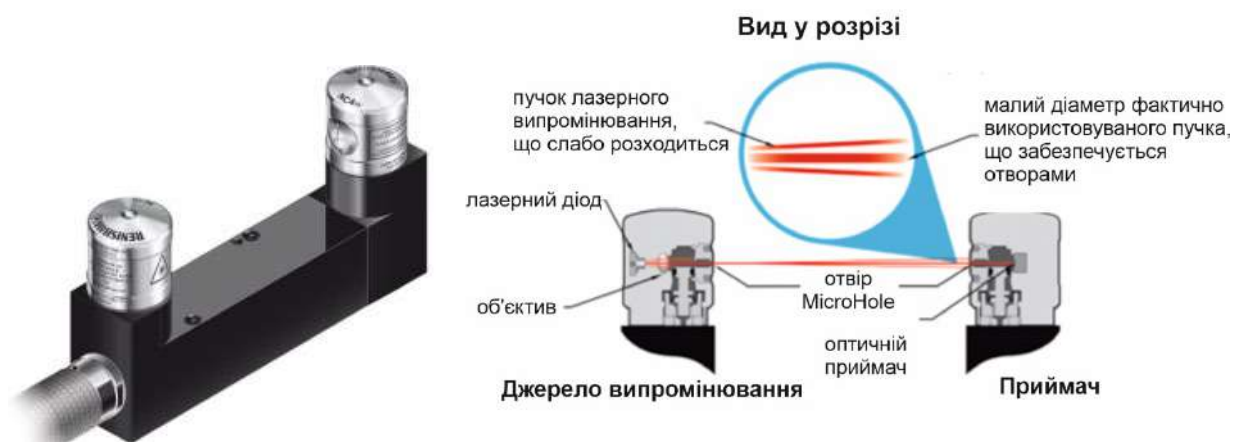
Схема роботи лазерного пристрою для налагодження інструменту
